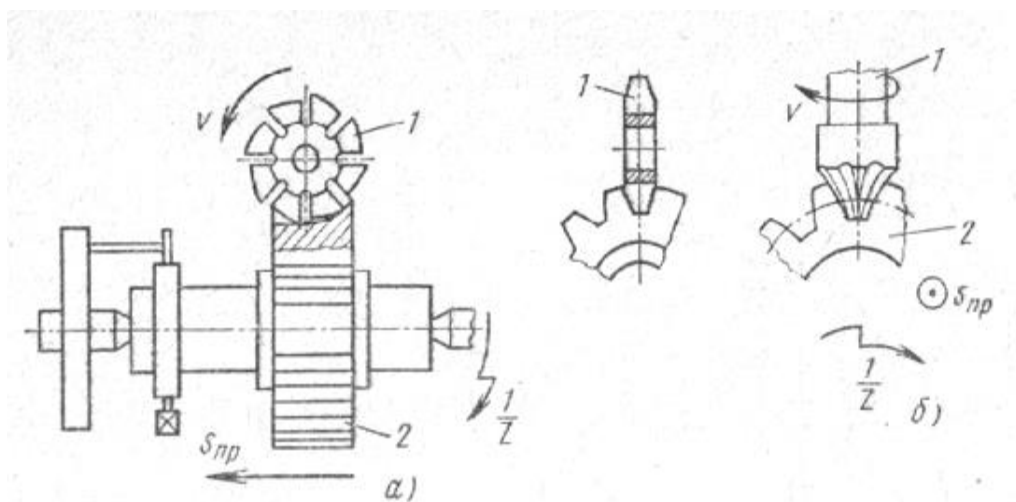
Фрезерование зубьев дисковыми и пальцевыми модульными фрезами
